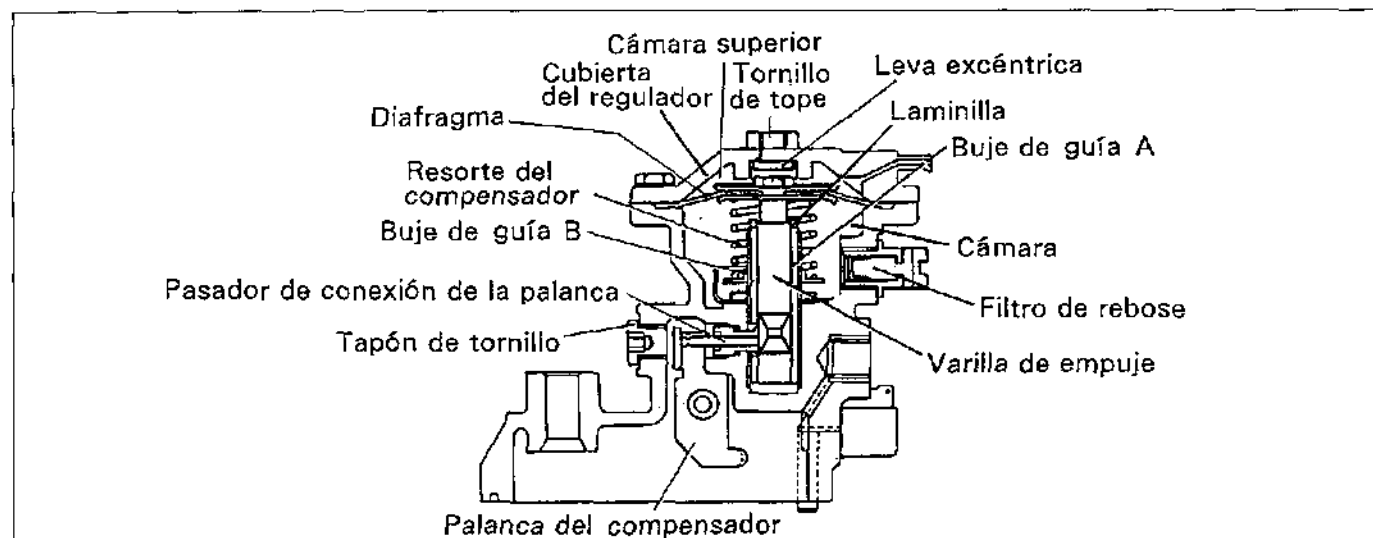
Construcción del compensador de turboalimentador (B.C.)
